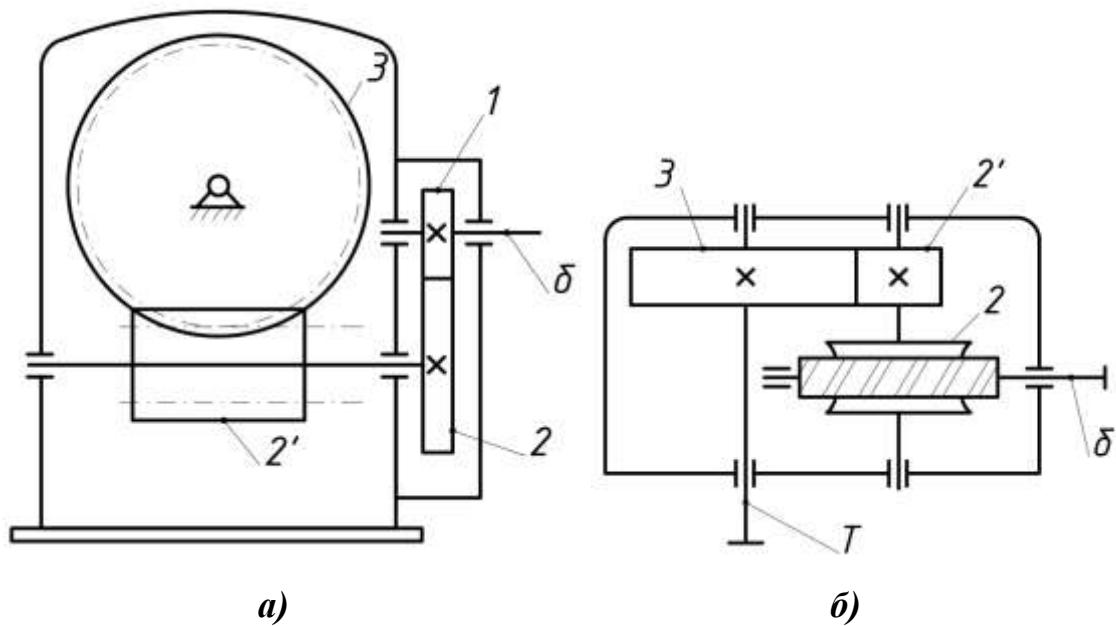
Кинематические схемы зубчато-червячных (а) и червячно-зубчатых (б) редукторов.
